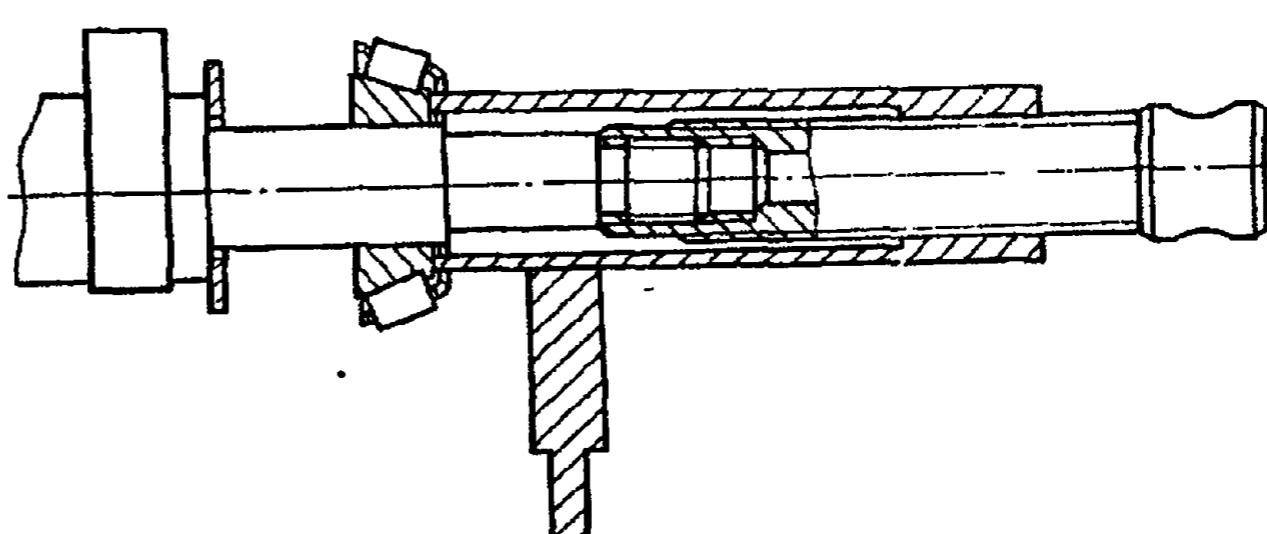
Приспособление И801.27.000 для установки подшипников кулачкового вала ТНВД
